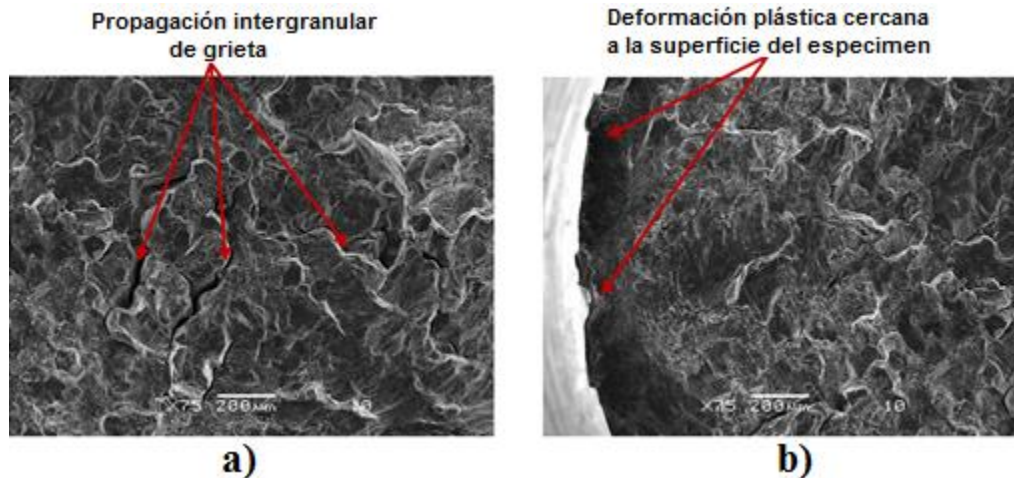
a) Propagación intergranular de grieta al centro del espécimen bajo cargas de torsión, b) alta deformación plástica en la sección angosta del espécimen.
